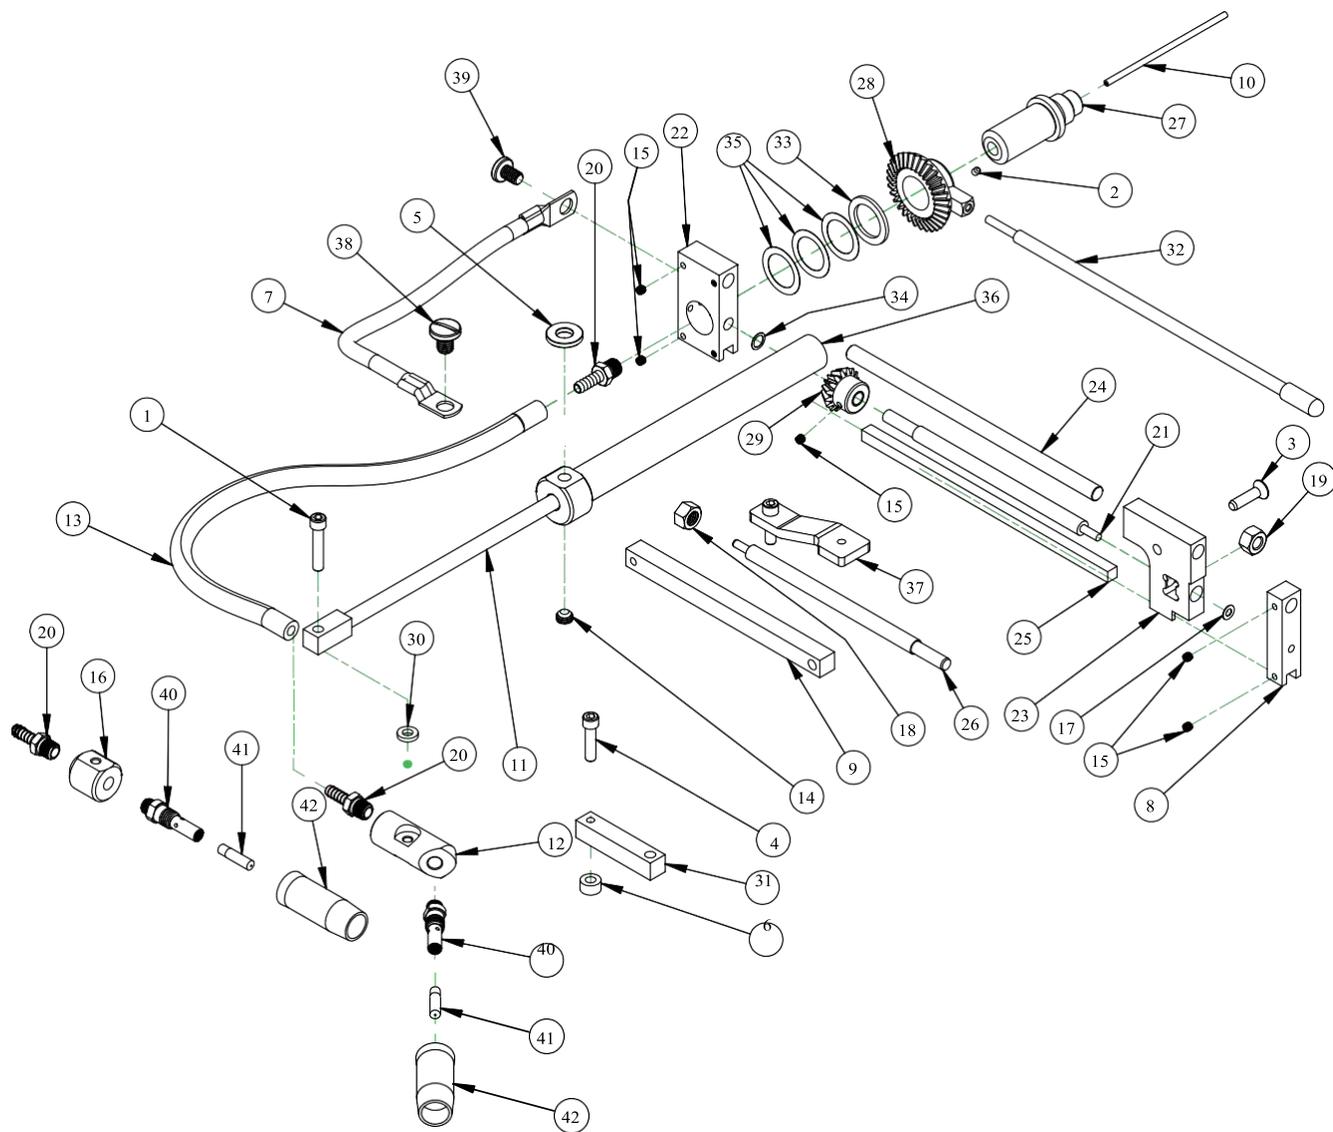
ГОРЕЛКА ДЛЯ НАПЛАВКИ ВНЕШНИХ ДИАМЕТРОВ 203 мм(8 ДЮЙМОВ) в сборе (КАТ. № 28186)
